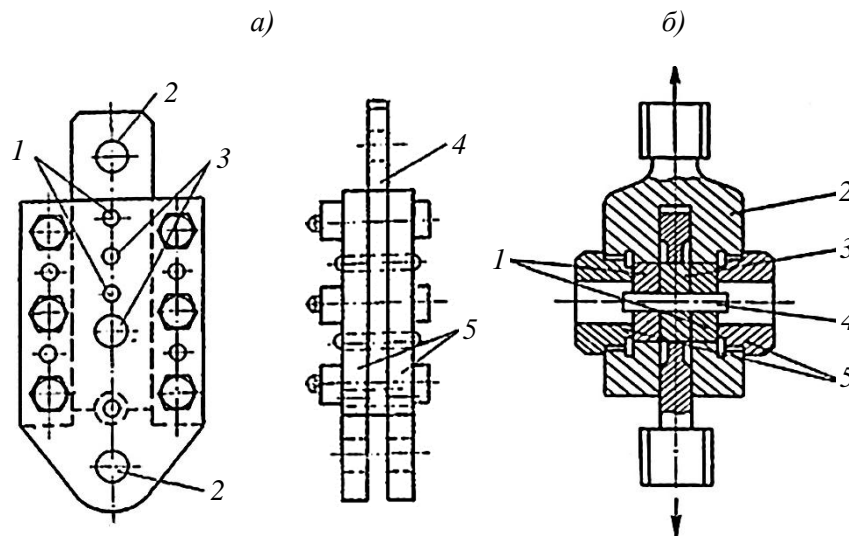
Схемы приспособлений типа соединения «вилка–проушина» для испытаний на двойной срез: а) 1 – отверстия для удаления выталкивателем частей разрушенного образца; 2 – отверстия для крепления приспособления в захватах испытательной машины; 3 – отверстия для образца; 4 – нож; 5 – щеки; б) 1 – щеки; 2 – корпус; 3 – нож; 4 – образец; 5 – вкладыш [2]
